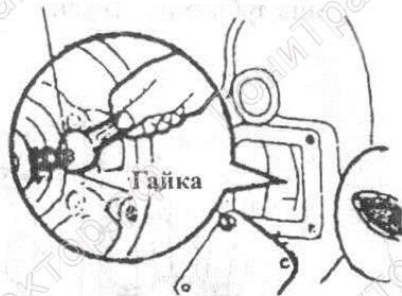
Регулировка зазора между отжимным кольцом и выжимным подшипником.
